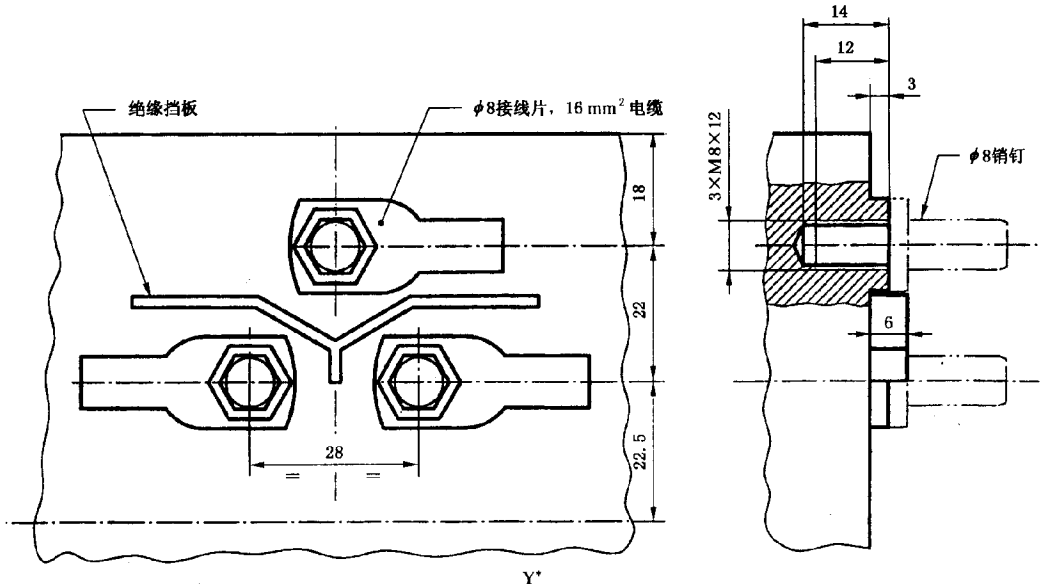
用于 J 型变压器连接的 3 个 M8 孔的尺寸和位置
